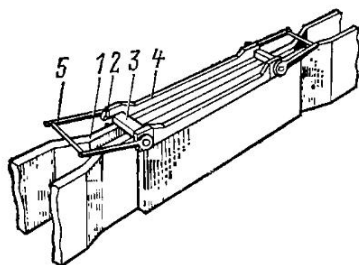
Кондуктор для пофазной сварки стыков секций магистральных шинопроводов.
